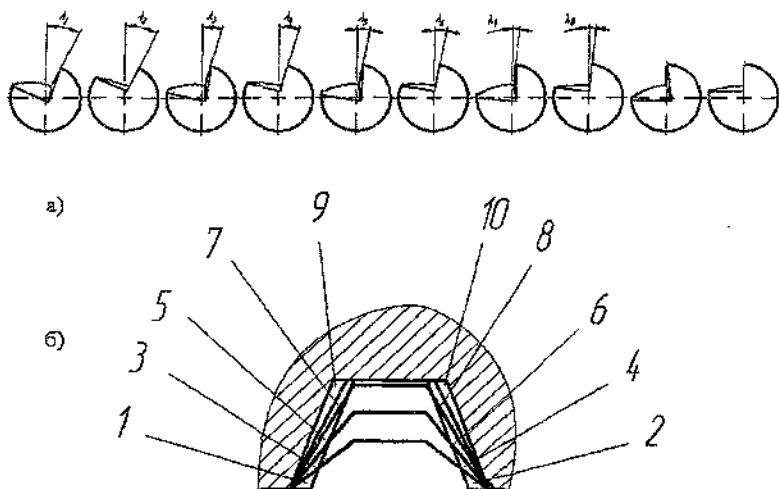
Схема протягивания зуборезными головками-протяжками с круглыми резами
